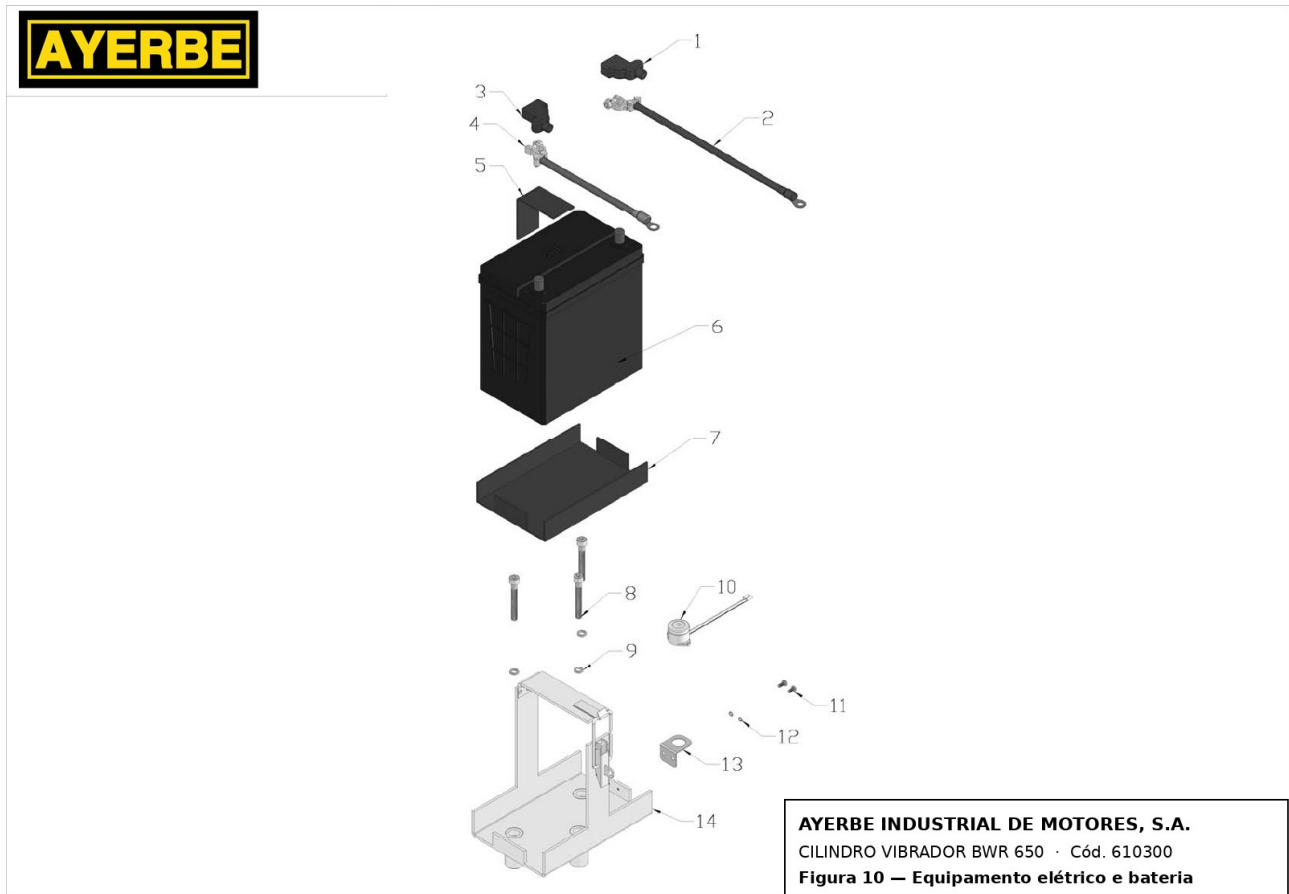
Vista explodida — Equipamento elétrico e bateria
